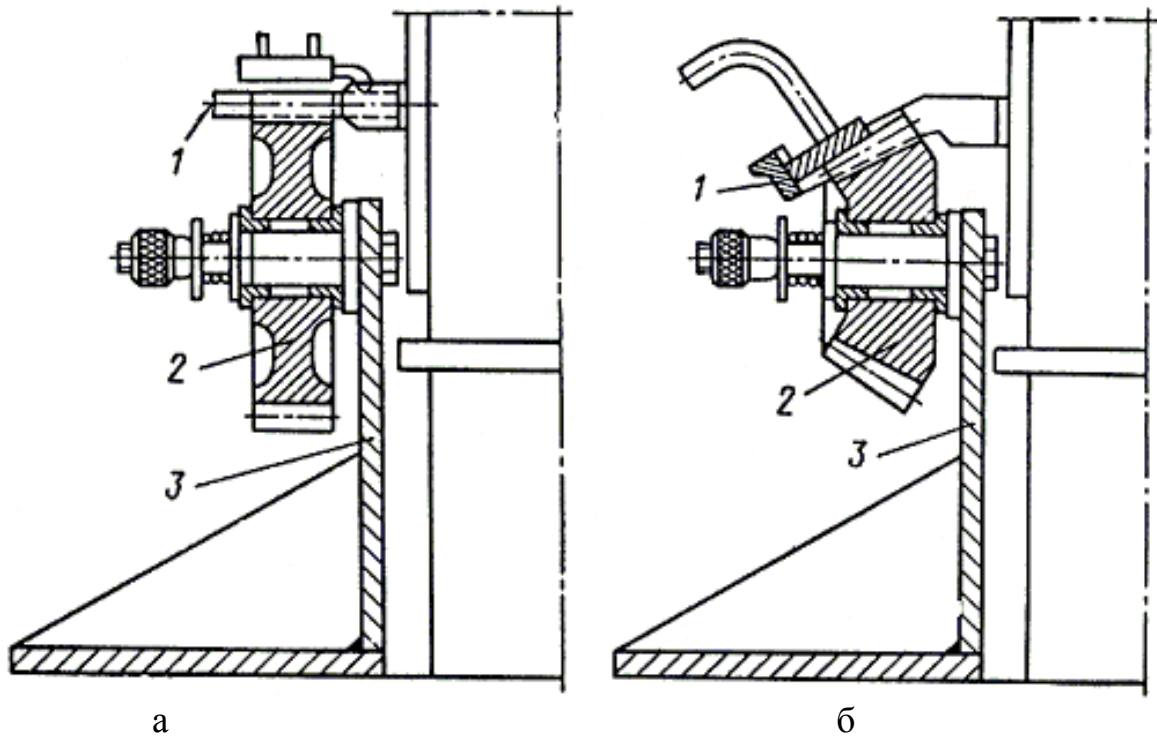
Схема послідовного високочастотного загартування зубів великих зубчастих коліс: а – пристрій для загартування циліндричних коліс; б – пристрій для конічних коліс; 1 – індуктор; 2 – зубчате колесо; 3 – пристрій для встановлення і повороту колеса.
